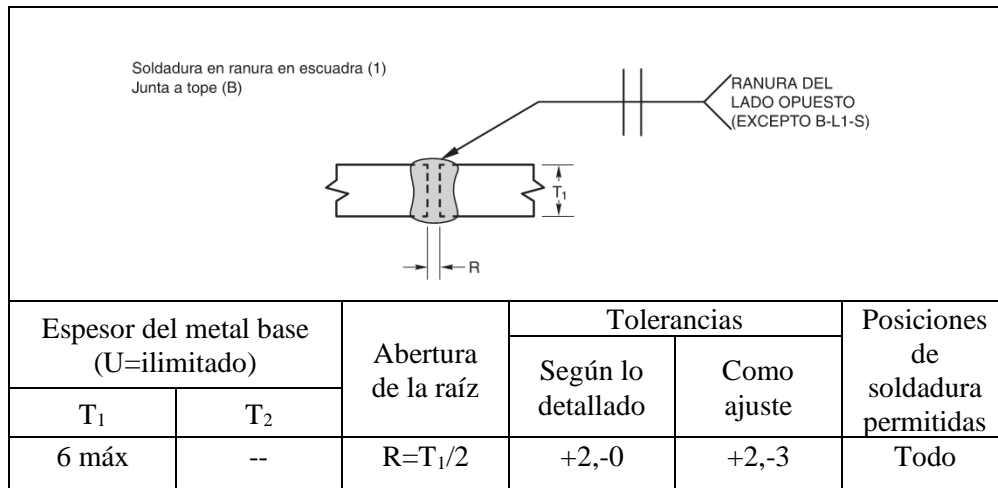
Detalles de la tope precalificada en milímetros
